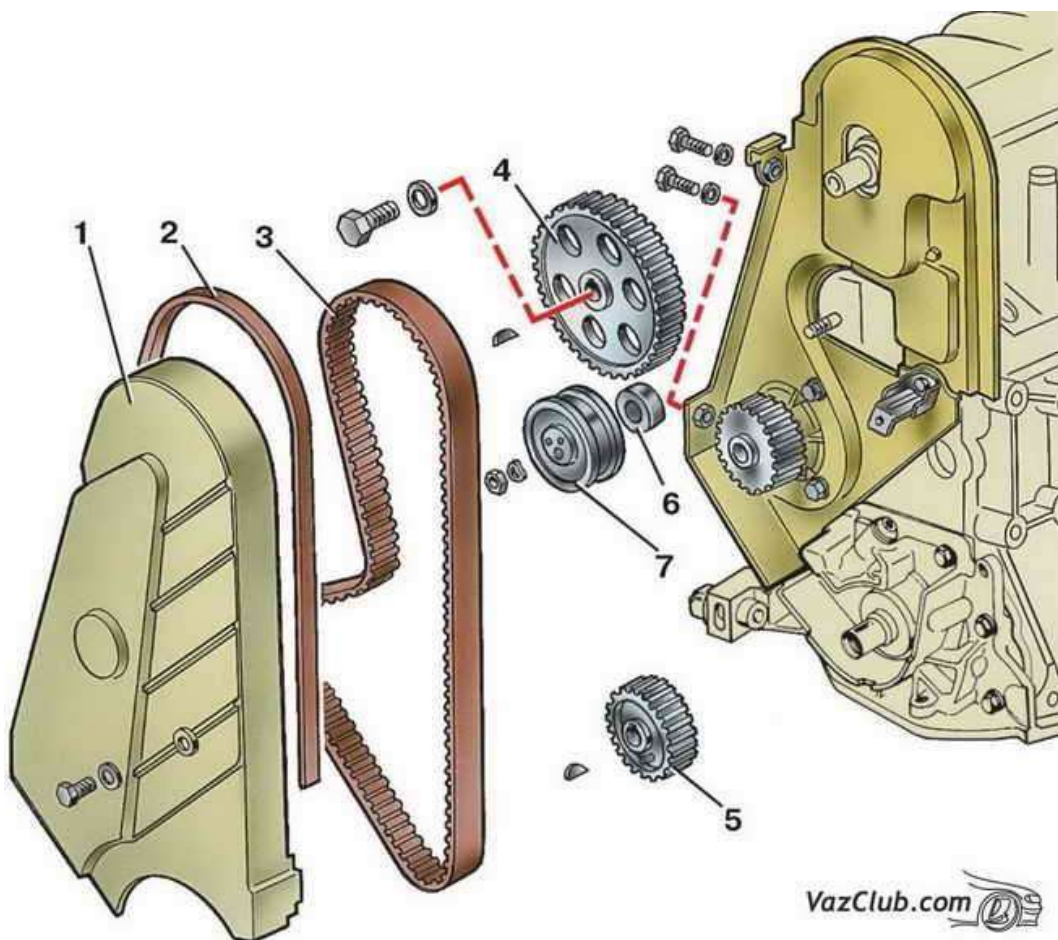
Снятие привода распределительного вала: 1 – передняя защитная крышка; 2 – резиновый уплотнитель; 3 – зубчатый ремень; 4 – шкив распределительного вала; 5 – зубчатый шкив коленчатого вала; 6 – дистанционная шайба; 7 – натяжной ролик
